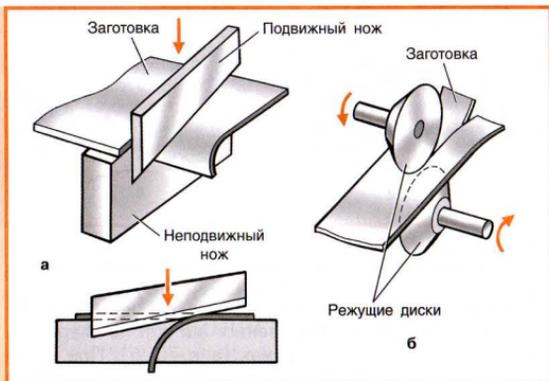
Резание листового металла механическими ножницами: а — гильотинными; б — дисковыми
